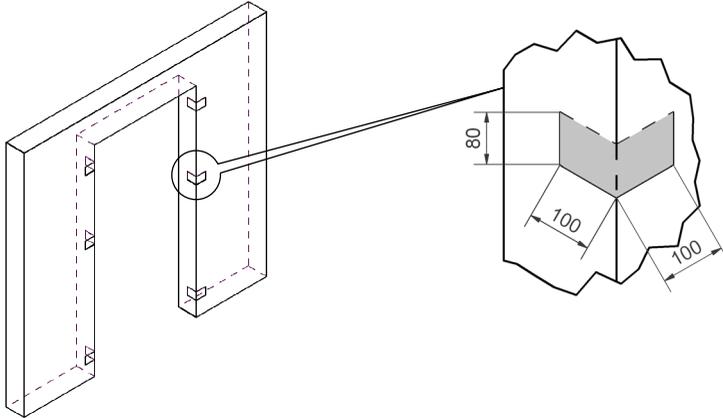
Befestigungsbereiche für Schweißnähte
